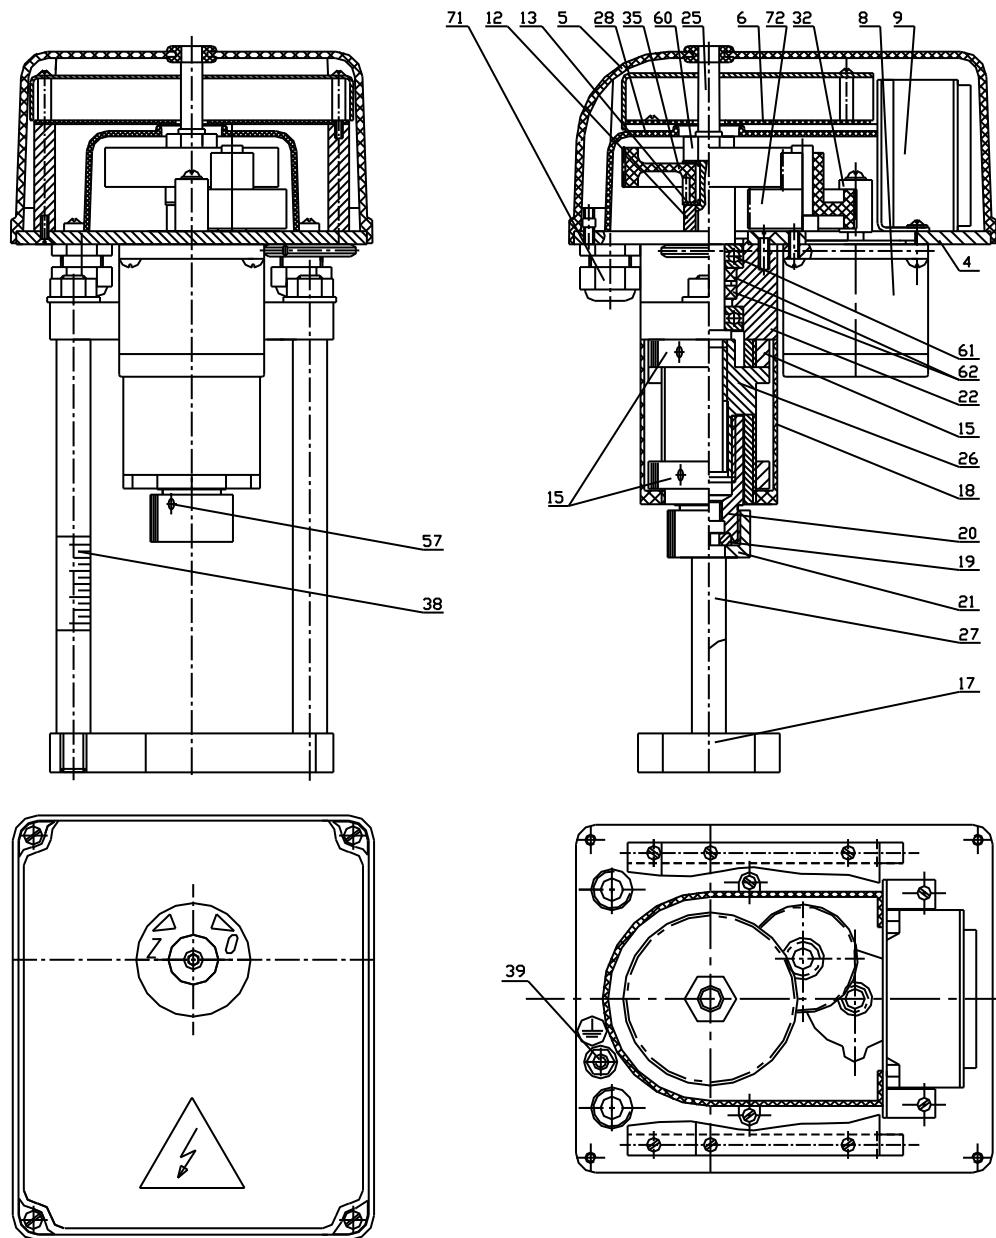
Устройство исполнительного механизма МЭП-3500/ХХ-30-В-Ф-57-35
